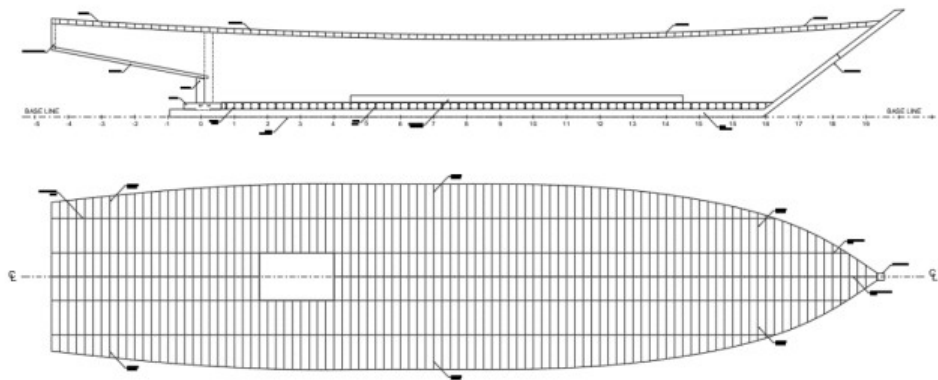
Construction Profil* Kapal Hang – Lengkir
